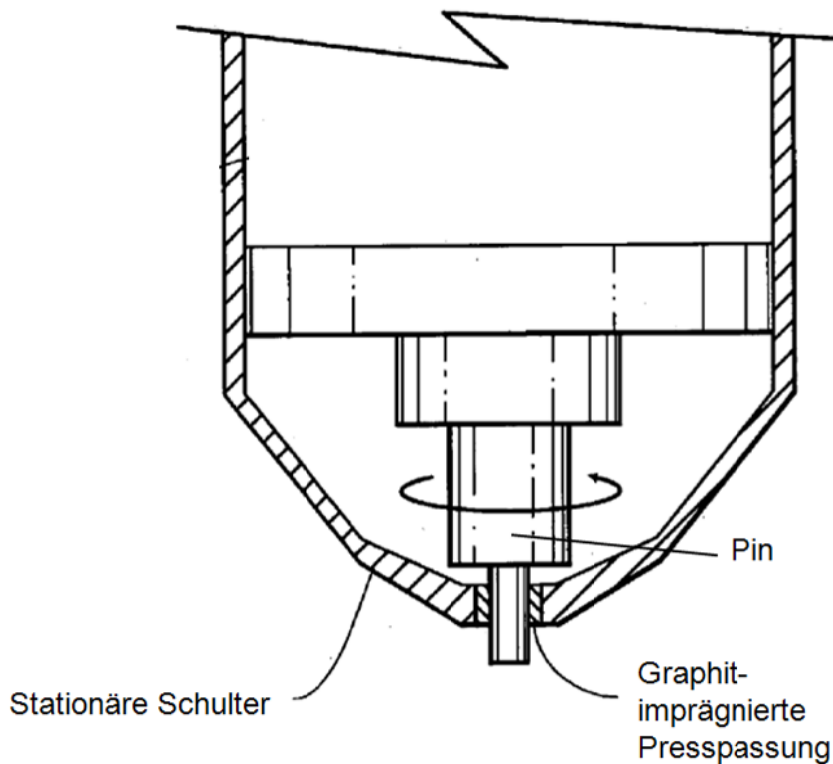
Prinzipskizze Patent FSW Tool für Polymere[1]
